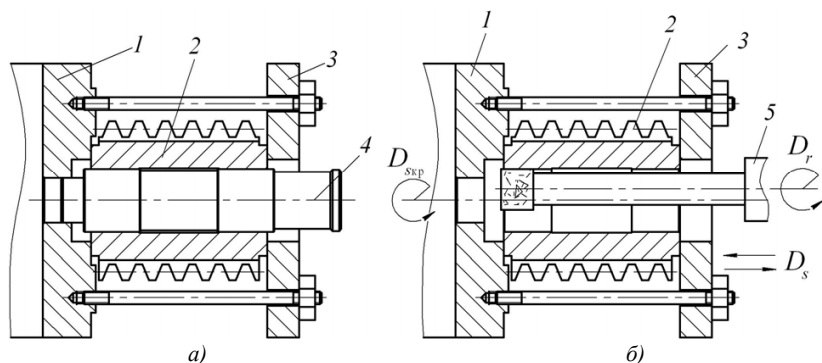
Шлифование отверстия заготовки червячной фрезы на внутришлифовальном станке: а) установка заготовки; б) шлифование отверстия: 1 – планшайба; 2 – заготовка; 3 – диск; 4 – контрольная оправка; 5 – оправка шлифовального круга
